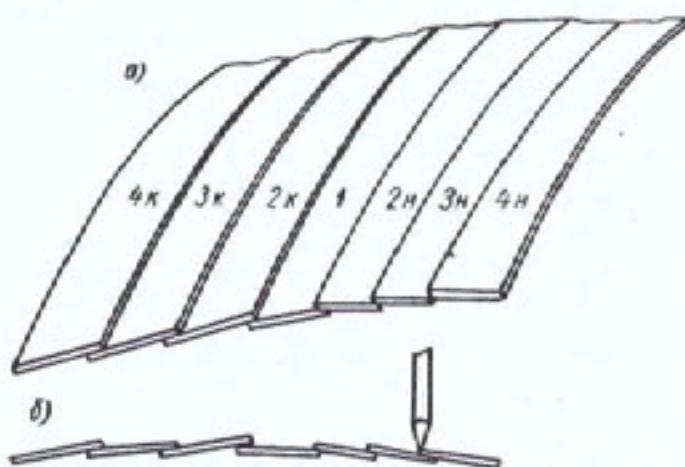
Пригонка полос шпона: а — укладка с перекроем; б — очерчивание кромок.
